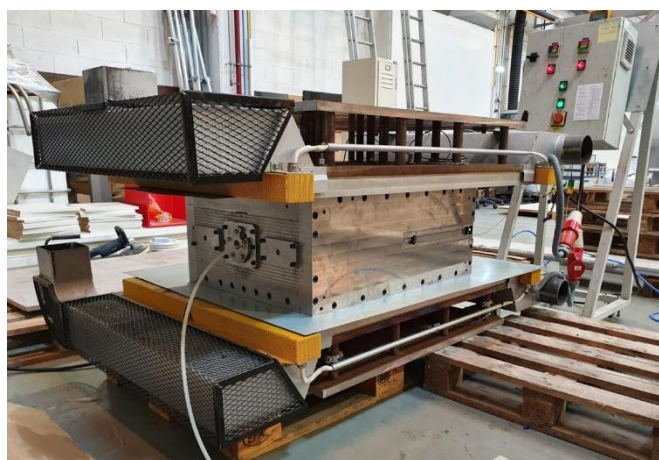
Setup do ensaio de aquecimento do molde.
